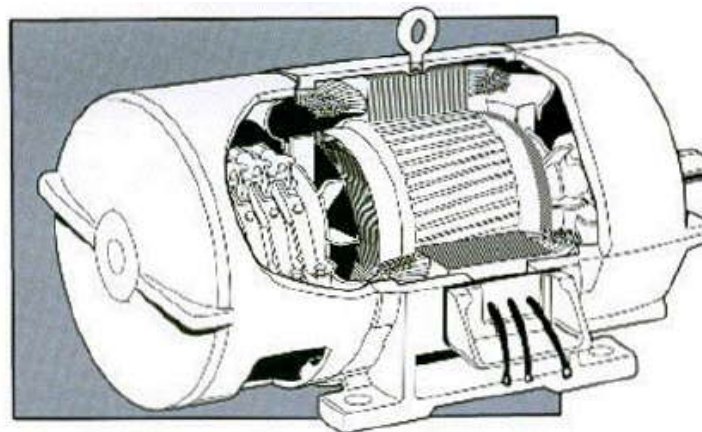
Machine asynchrone à rotor bobiné [Poi 2003 a]
